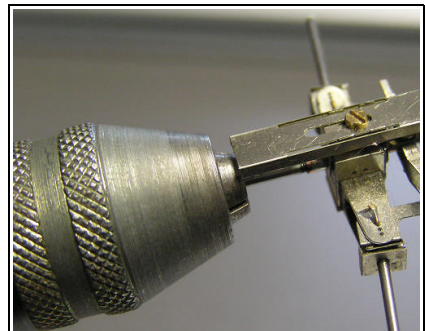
Probelauf von Hand und dann mit der Bohrmaschine mit wenig Drehzahl machen. Alle beweglichen Stellen etwas ölen.
